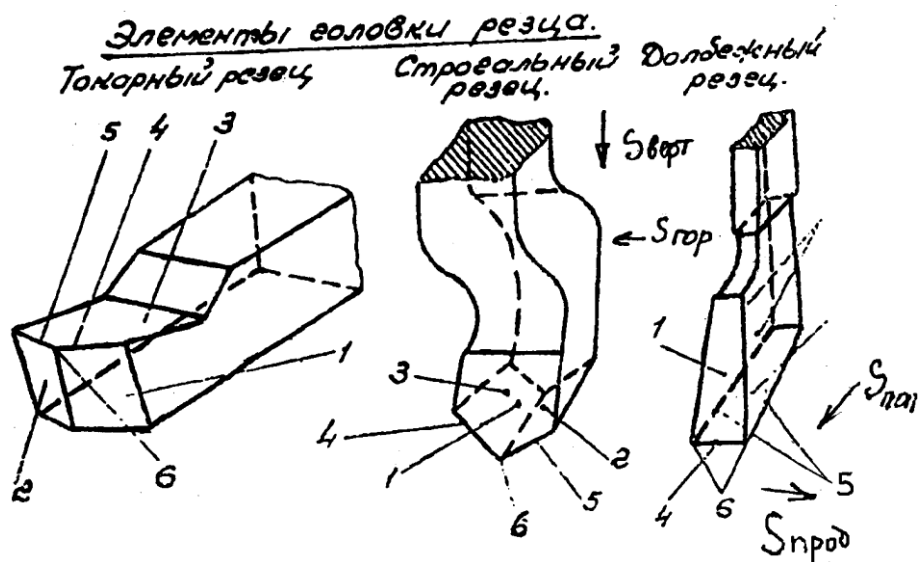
Элементы головки резца 1 — главная задняя поверхность; 2 — вспомогательная задняя поверхность; 3 — передняя поверхность; 4 — главное режущее лезвие; 5 — вспомогательное режущее лезвие; 6 — вершина резца.
